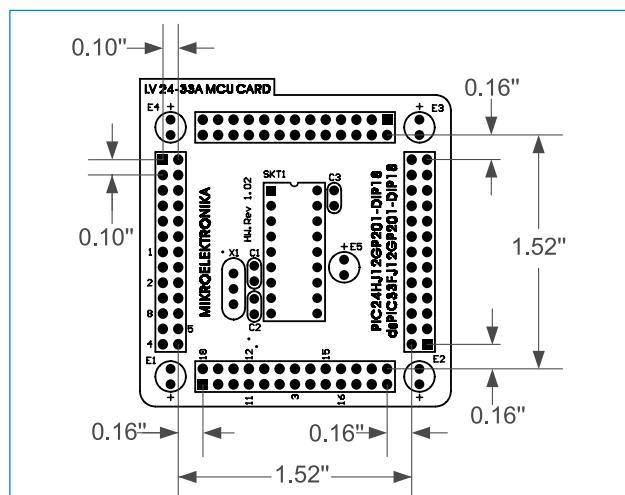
Dimensiones de la tarjeta MCU para la *MCU Card 9
